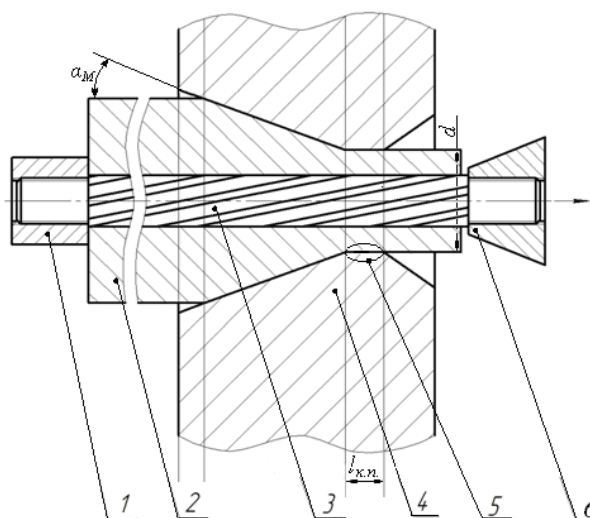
Схема обжатия трубчатой заготовки в гладкой конической матрице:
